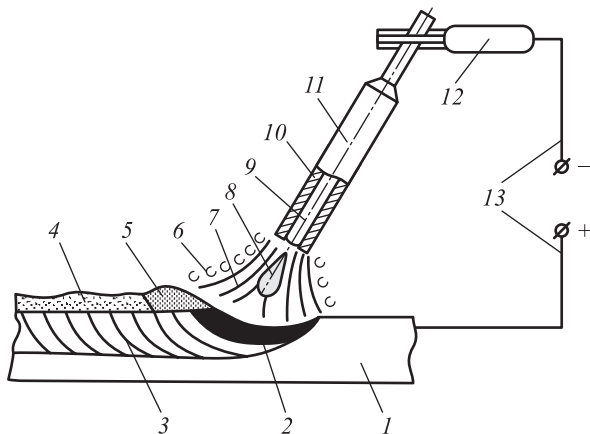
Схема ручной дуговой сварки:
